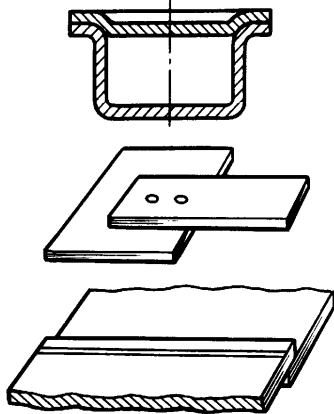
Сварные соединения, выполненные ультразвуковой сваркой
